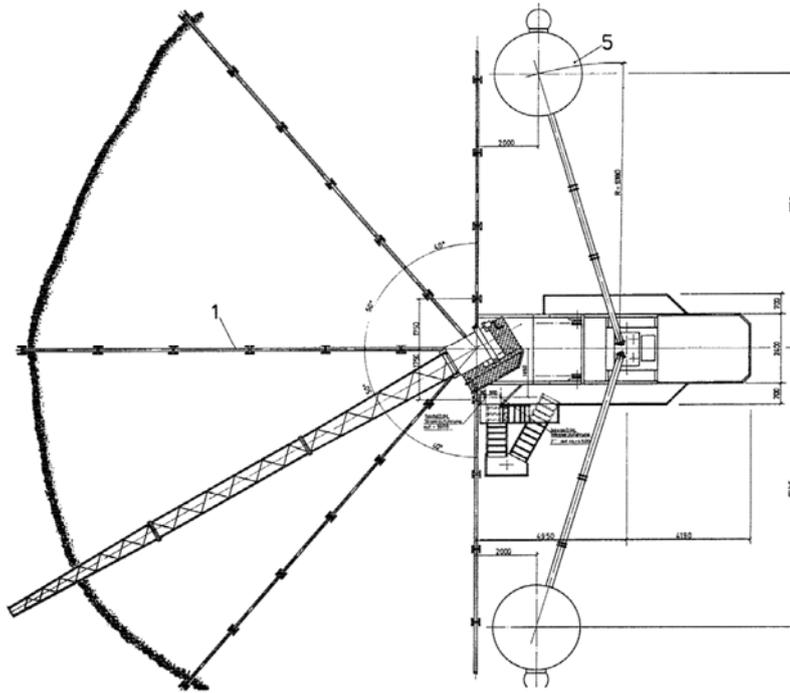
Betonmischanlage: ELBA-Mixcenter EMC 45 / EMC 60 [7]
